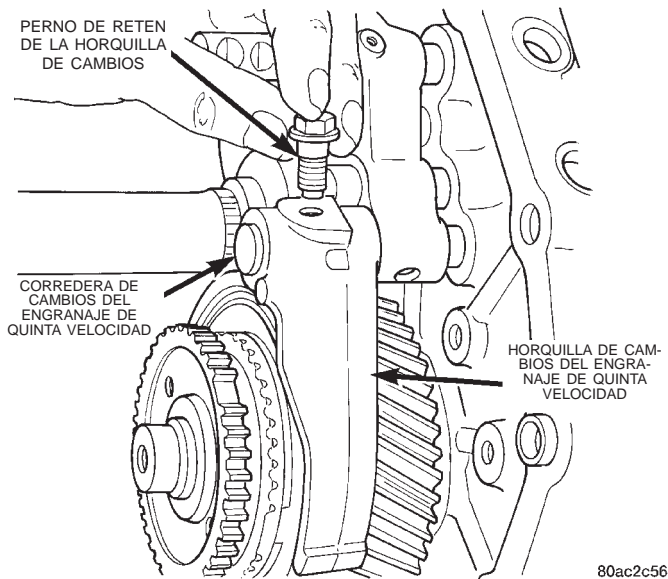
Desmontaje del perno de retén de la horquilla de cambios
